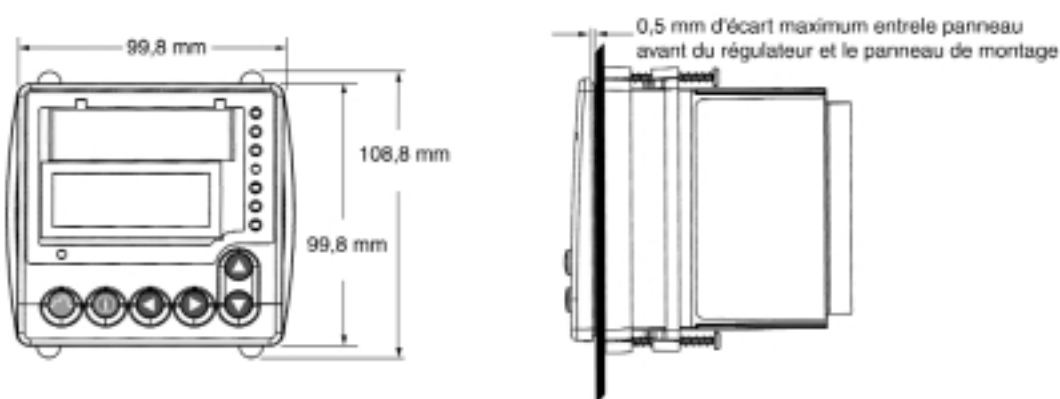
Dimensions, vue de face et dimension de l'écart du joint.
